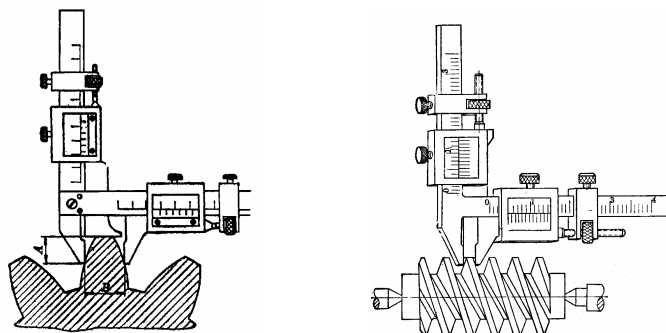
齿厚游标卡尺测量齿轮与蜗杆
